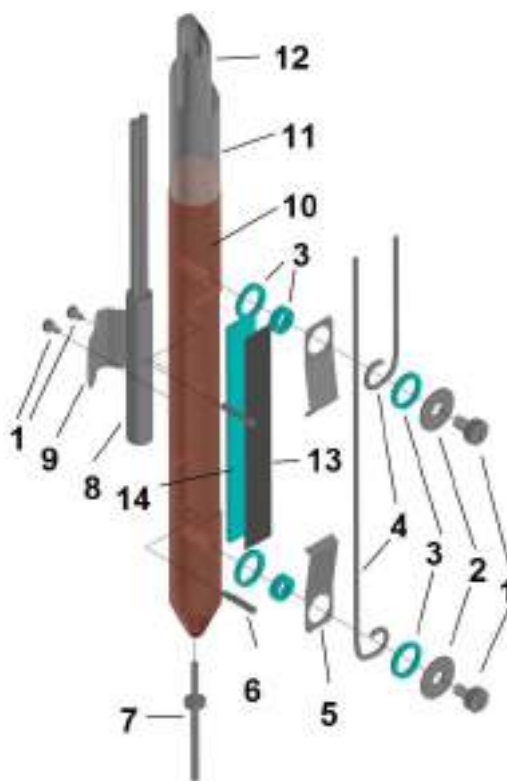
Внешний вид держателя образца с токоподводящей навеской
